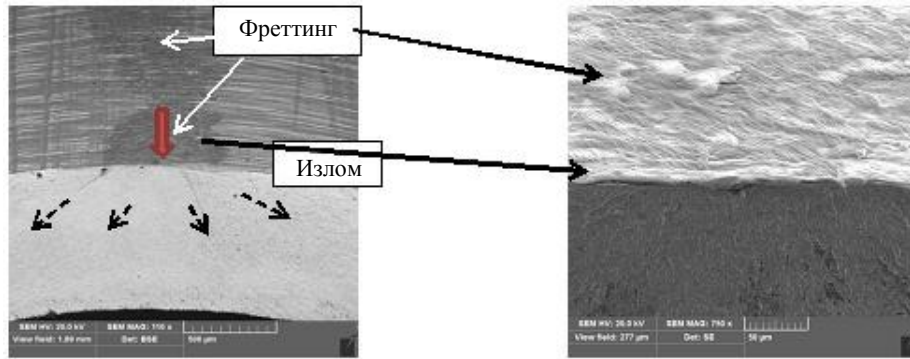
Вид усталостной трещины по месту участка фреттинг-коррозии на поверхности трубы со шлифованной наружной поверхностью. Трещина образовалась в процессе усталостных испытаний в условиях возникновения фреттинга
